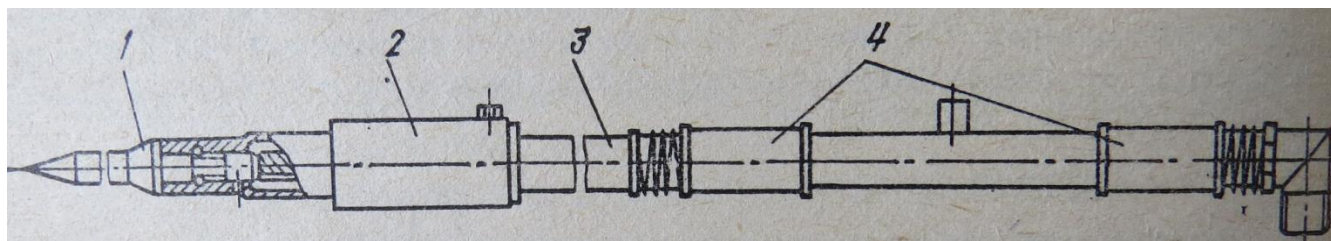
Принципова схема пристрою ОК-3 для прибирання заколів:
